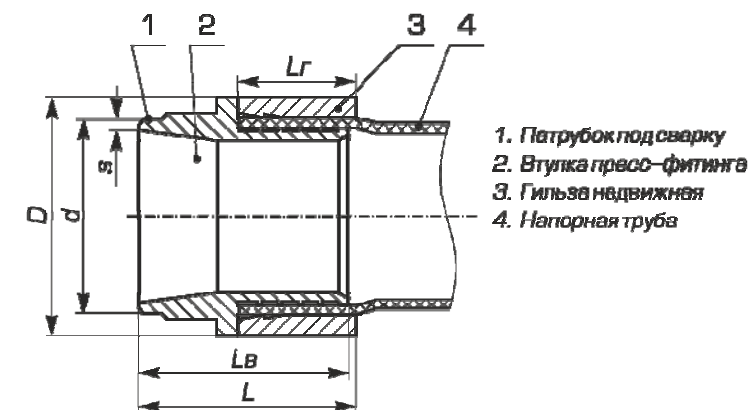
Пресс-фитинг под сварку ИЗОПРОФЛЕКС
